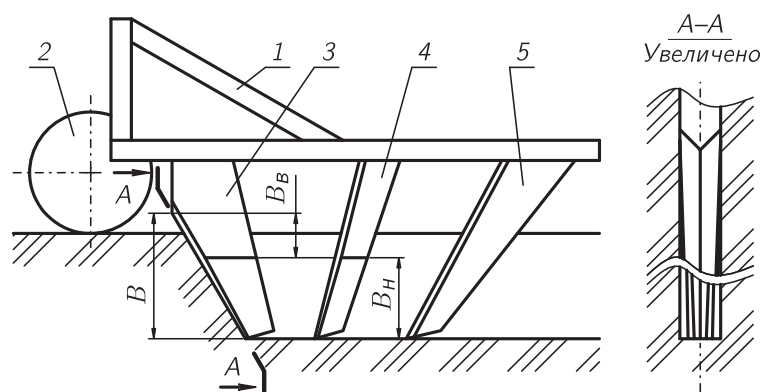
Щелеватель для нарезки направляющих щелей в почве: 1 — рама; 2 — опорное колесо; 3, 4 и 5 — ножи-щелерезы
